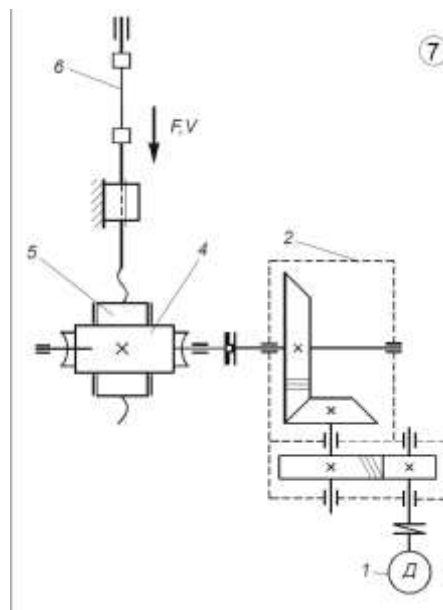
Кінематична схема приводу: 1- двигун, 2 – редуктор; 4 – черв'ячна передача; 5 – гвинт; 6 – зразок.
